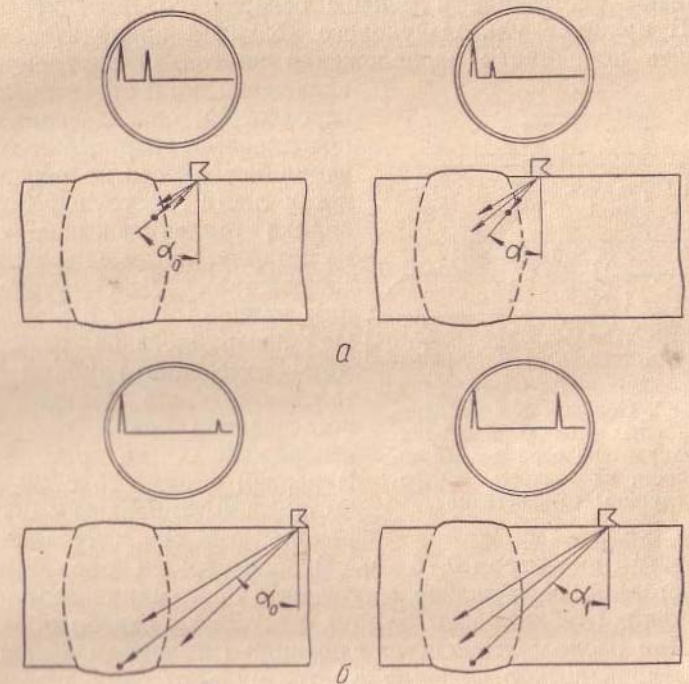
Выявление дефектов при контроле сварных соединений большой толщины.
